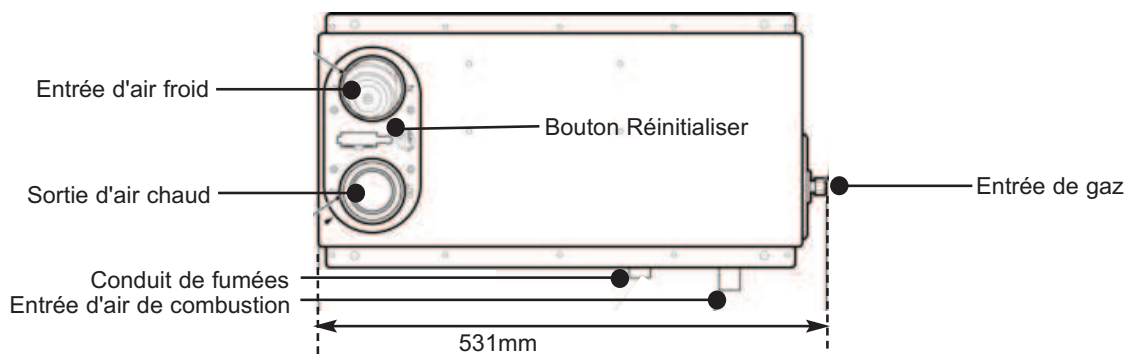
Installation sous plancher - Vue de plan - SH2211 ou SC2211
